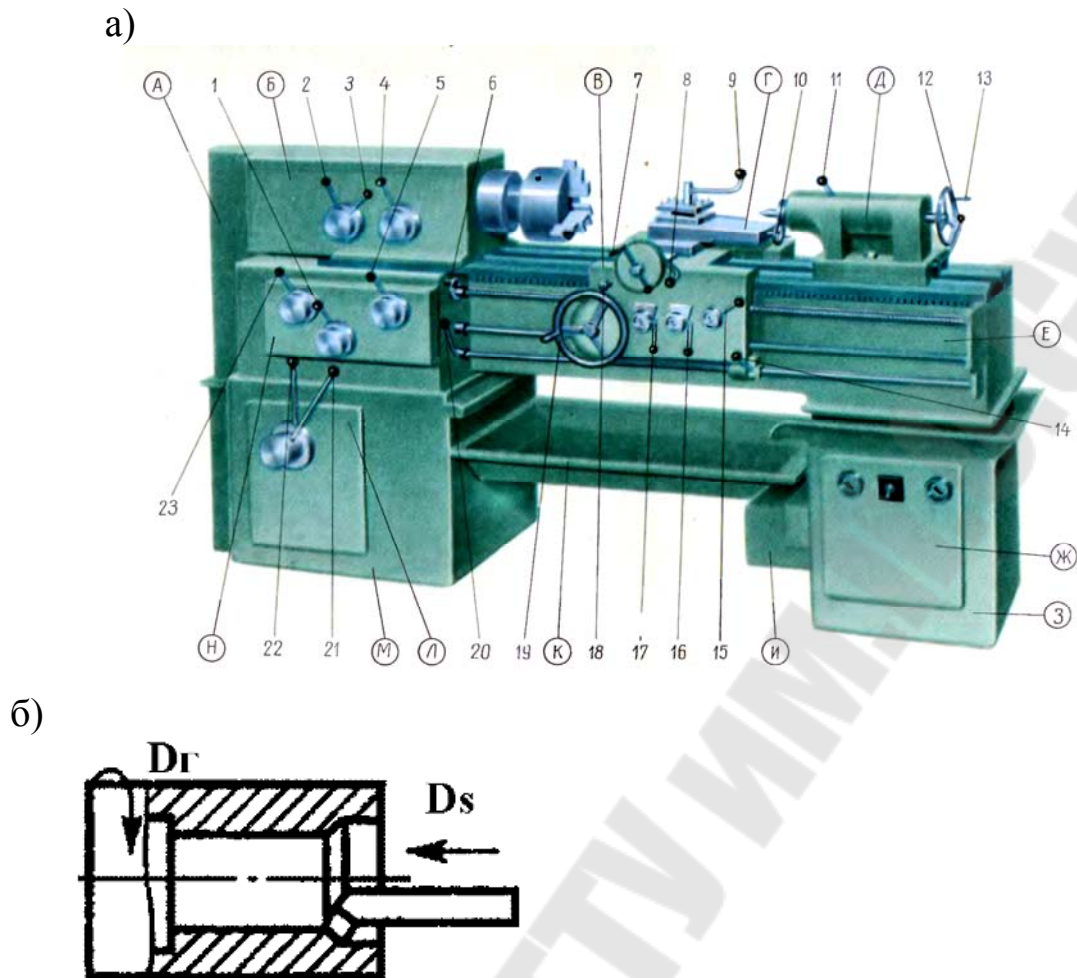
Общий вид токарного станка (а) и схема растачивания отверстия (б)
